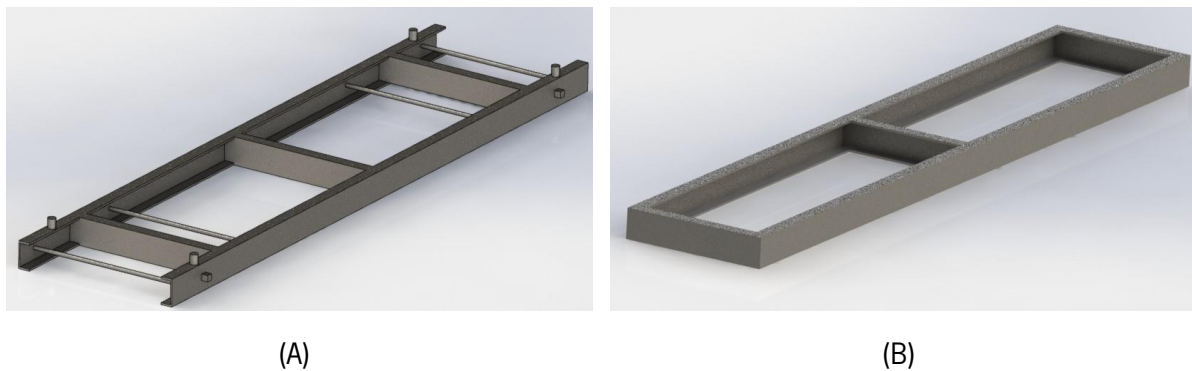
A – Estrutura metálica do acessório manual; Figura 4.3 B – Estrutura base equipamento projetado
